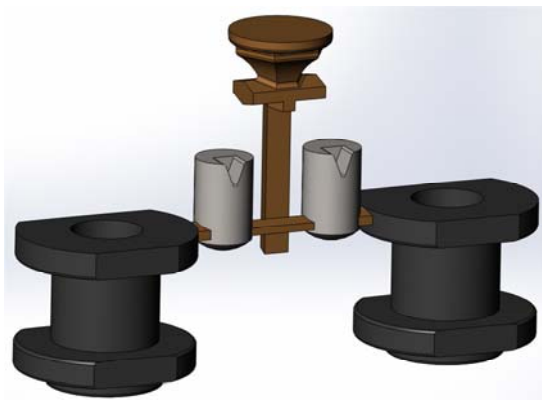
Отливки «Корпус» с литниково-питающей системой
